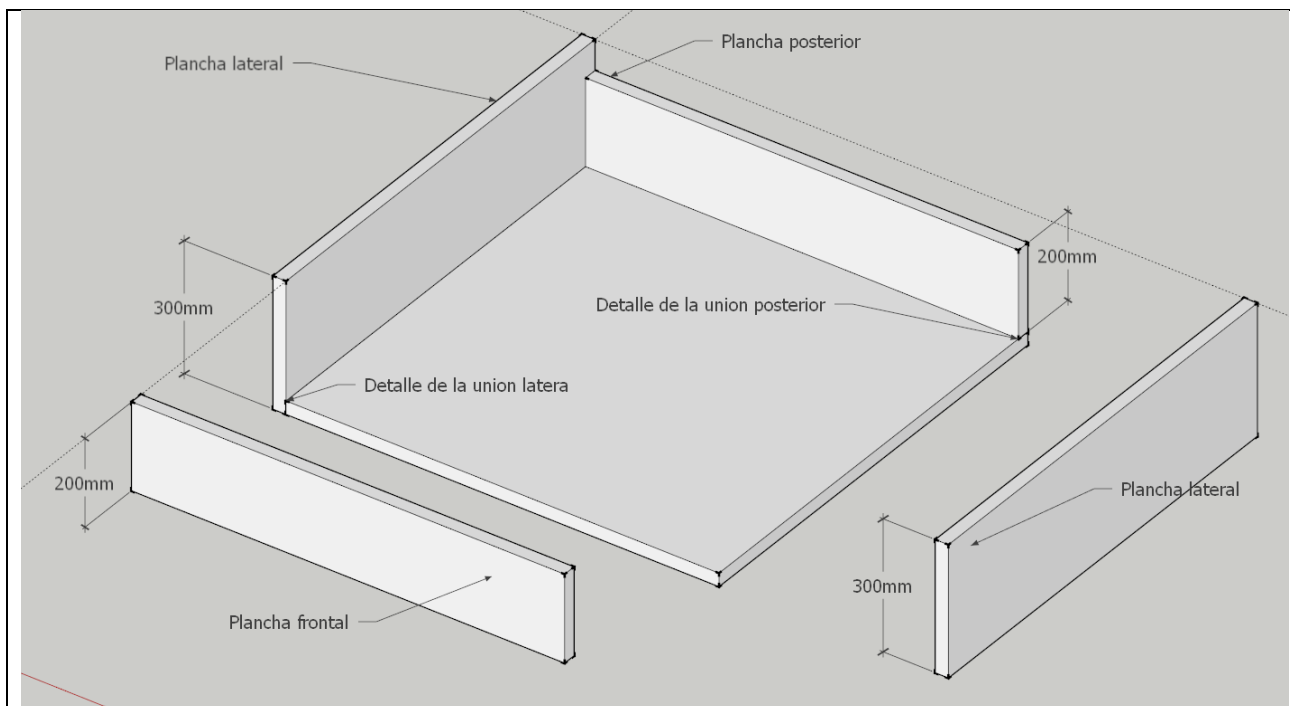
Construcción parcial del cuerpo del secadero (observar los detalles de unión lateral).
